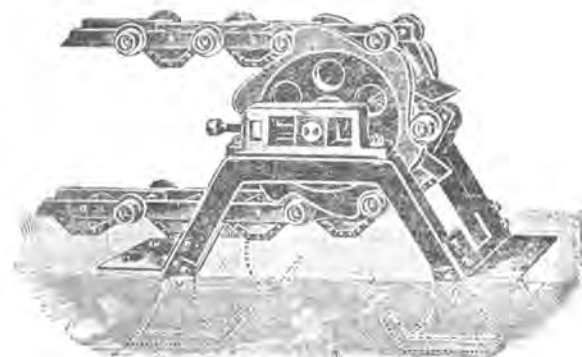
Винтовое натяжное приспособление для горизонтальных транспортеров.
